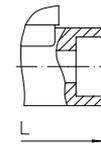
/682/683/684....3 mit Schweißmuffen
